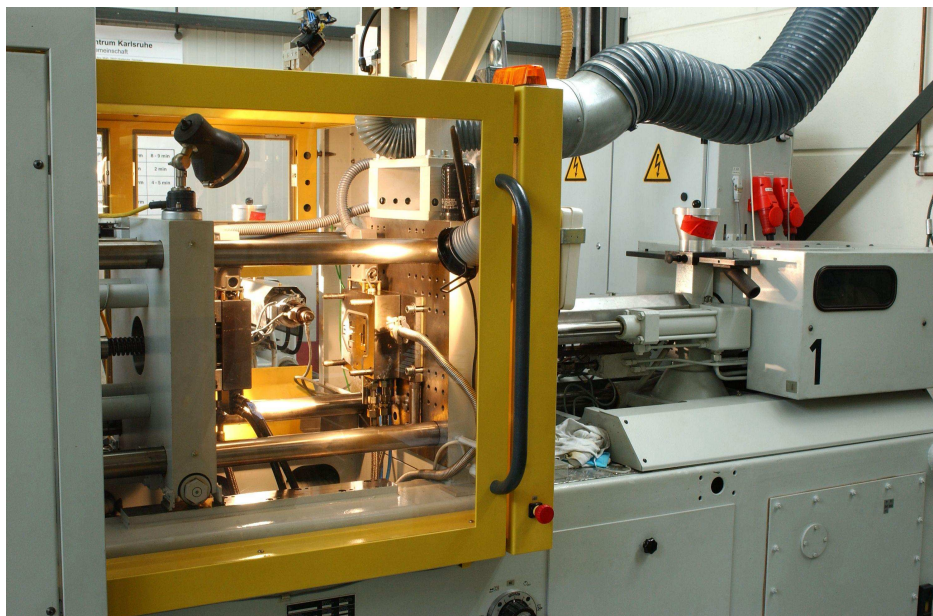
Zweikomponenten-Spritzgießmaschine, bestückt mit 2K-PIM-Werkzeug
